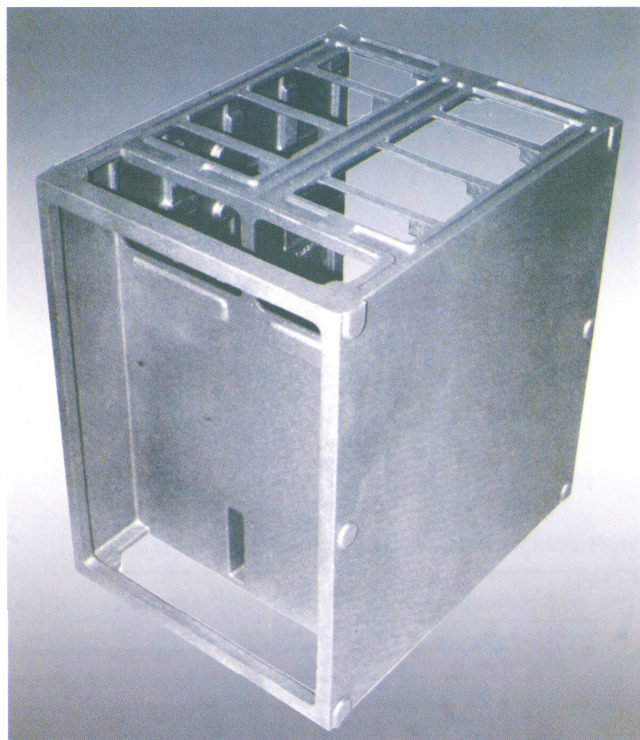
Корпус. Материал — Al-Si 12, масса — 33 кг, габариты — 650x610x470 мм
